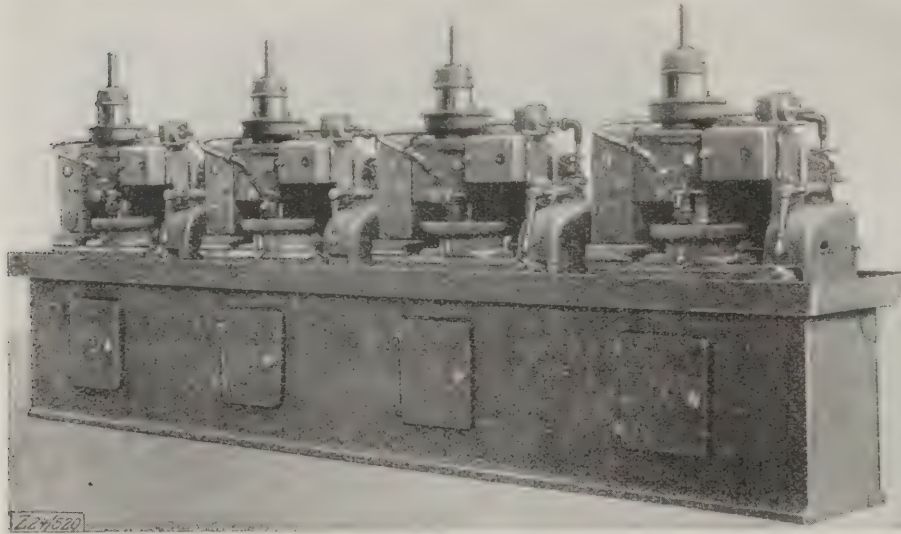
Schnellaufende Stirnrad-Abwälzhobelmaschine der Zimmermann-Werke, A.-G., Chemnitz.
